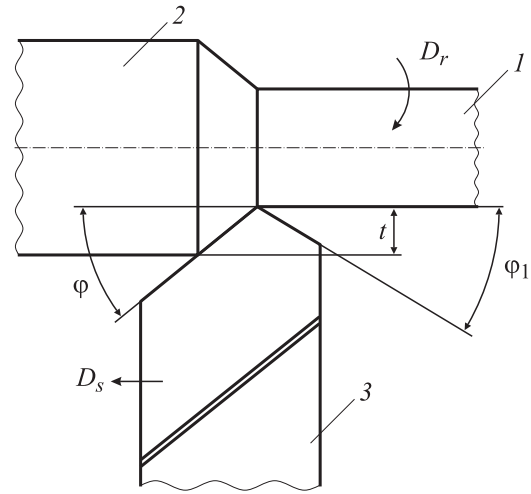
Элементы режима резания при точении. D_r — главное движение (вращательное движение заготовки), D_s — движение подачи (прямолинейное поступательное движение режущего инструмента), 1 — обработанная поверхность заготовки, 2 — обрабатываемая поверхность заготовки, 3 — режущий инструмент, φ — главный угол в плане, φ_1 — вспомогательный угол в плане, t — глубина резания.
